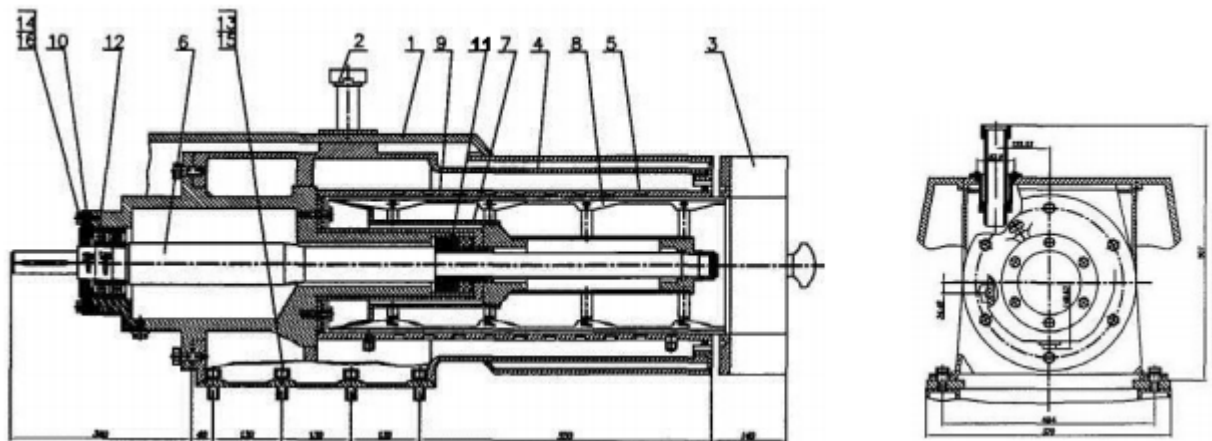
Збивач масловиготовлювача: 1 - корпус; 2 - штуцер подачі вершків; 3 - рукав; 4 - теплообмінна сорочка; 5 - сітчаста вставка; 6 - вал; 7 - корпус біла; 8 - лопата; 9 - циліндр; 10 - кришка; 11, 12 - підшипник; 13, 14, 15, 16 - болтове кріплення
